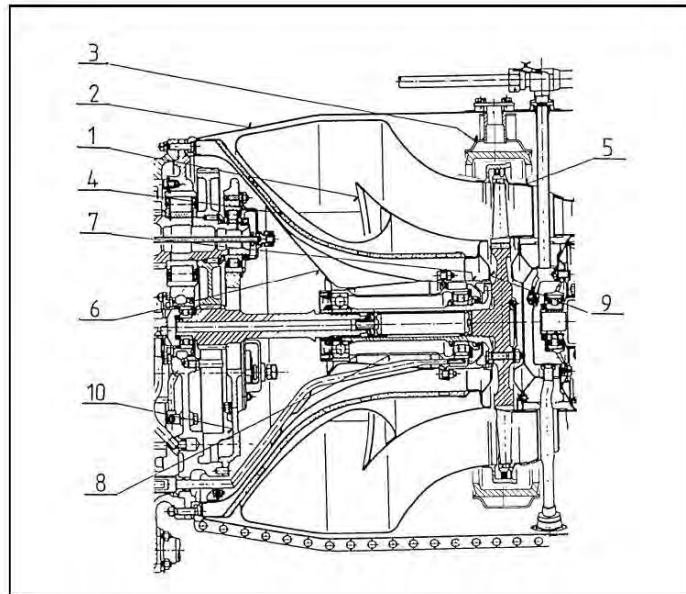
il *PT shaft* ed il *quill shaft* all'interno del *supporting cone*, tra *power turbine* e *reduction gearbox* (ingrandimento).
